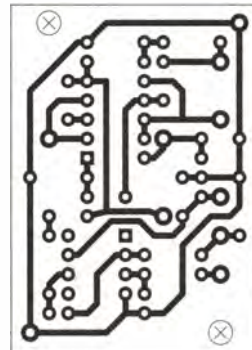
Layout der Ansteuerung; Maße 33 mm x 45,7 mm, M 1:1
